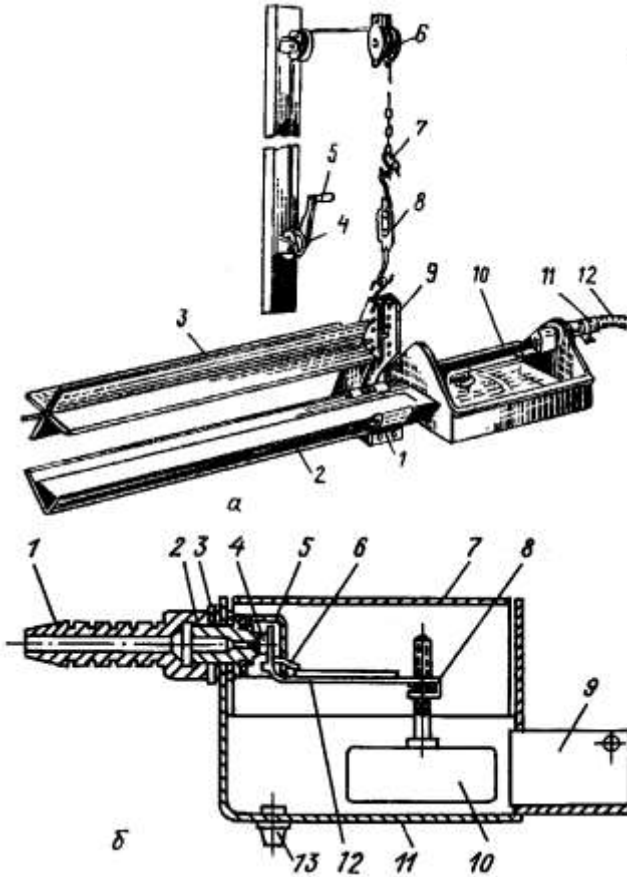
Жолобкова автонапувалка для птахів АП-2: а – загальний вигляд; 1-накладка; 2-жолоб; 3-вертушка; 4-лебідка; 5-рукоятка; 6-блок лебідки; 7-підвіска; 8-стяжка; 9-кронштейн; 10-корпус поплавкової камери; 11-хомут; 12-шланг; б-поплавкова камера: 1-штупцер; 2-корпус; 3-гайка; 4-клапан; 5-козирьок; 6-стопор; 7-кришка; 8-регулювальна гайка; 9-жолоб; 10-поплавок; 11-корпус; 12-важіль клапана; 13-пробка.
